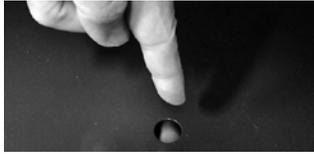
Tôle de fond/support de fond avec évidement rond
